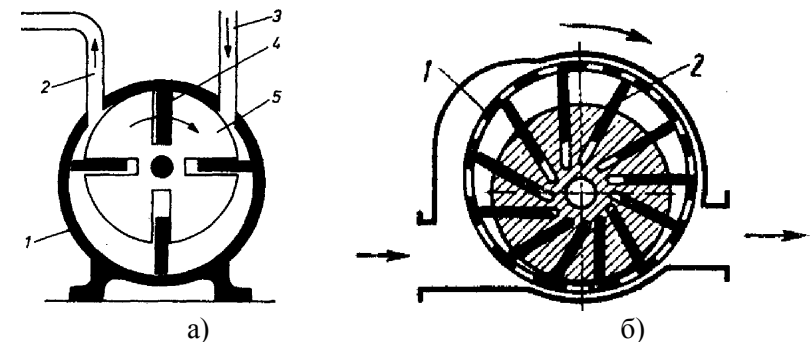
Схемы пластинчатых вакуумных насосов: а) четырехпластинчатый (1 – корпус; 2 – выхлопной патрубок; 3 – патрубок всасывающий; 4 – пластина; 5 – ротор); б) многопластинчатый с беговыми кольцами (1 – кольцо беговое; 2 – пластина)
